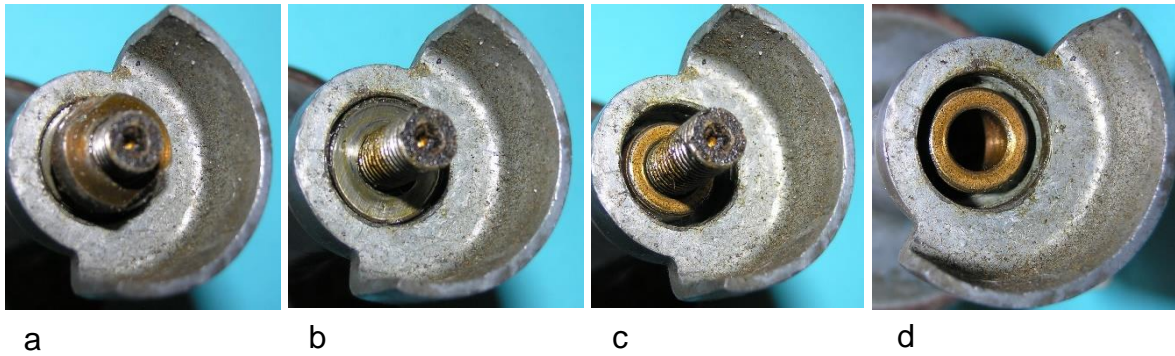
Bestückung des Wellenendes: a) Kontermutter, b) Anlaufscheibenkaskade, c) Gleitlager mit Welle, d) Stirnseite des Gleitlagers
